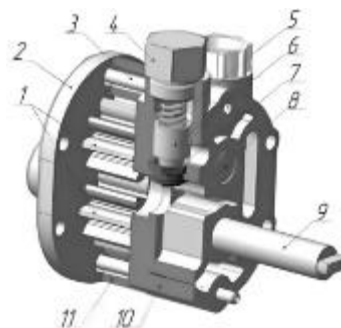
Живильний агрегат : 1.– блоки шестерень; 2, 10 - кришка; 3 - шпилька; 4 - гайка; 5, 6, 7 – клапанний вузол; 8, 9 - вали; 11 - основа
